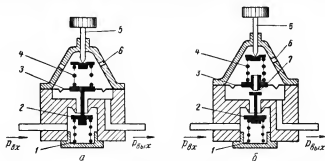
6. Редукторы давления воздуха пневматических регуляторов.
